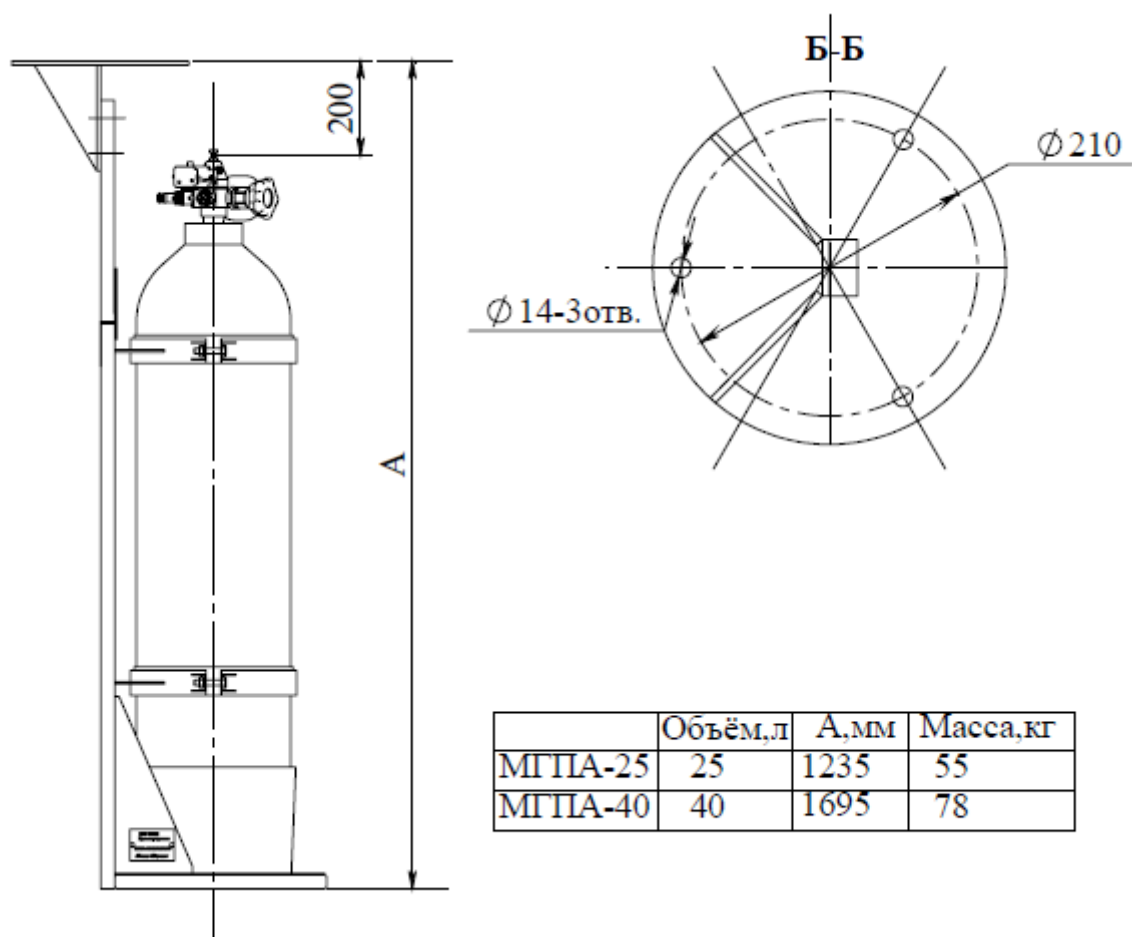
Общий вид, габаритные и присоединительные размеры МГПА объемом резервуара 25 и 40 л
